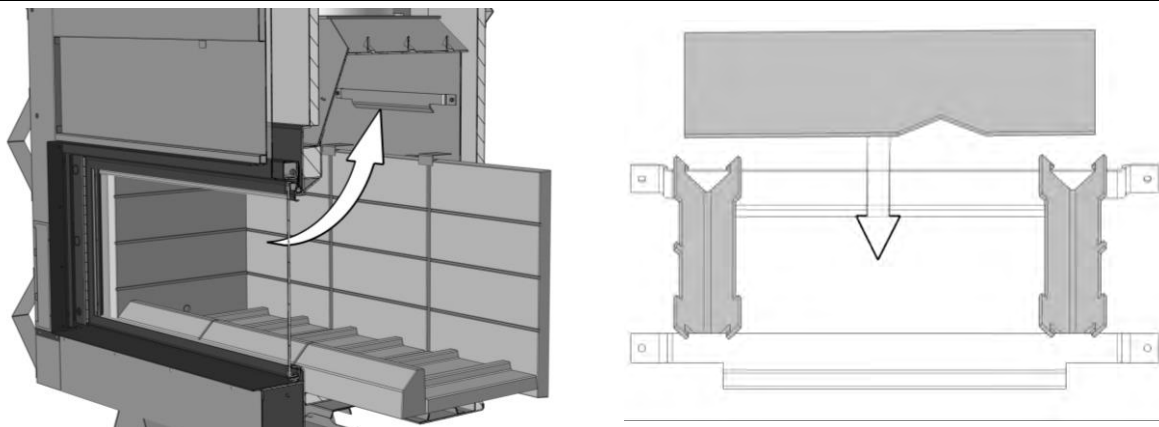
| INSTALLATION DU DÉFLECTEUR DE FUMÉE
